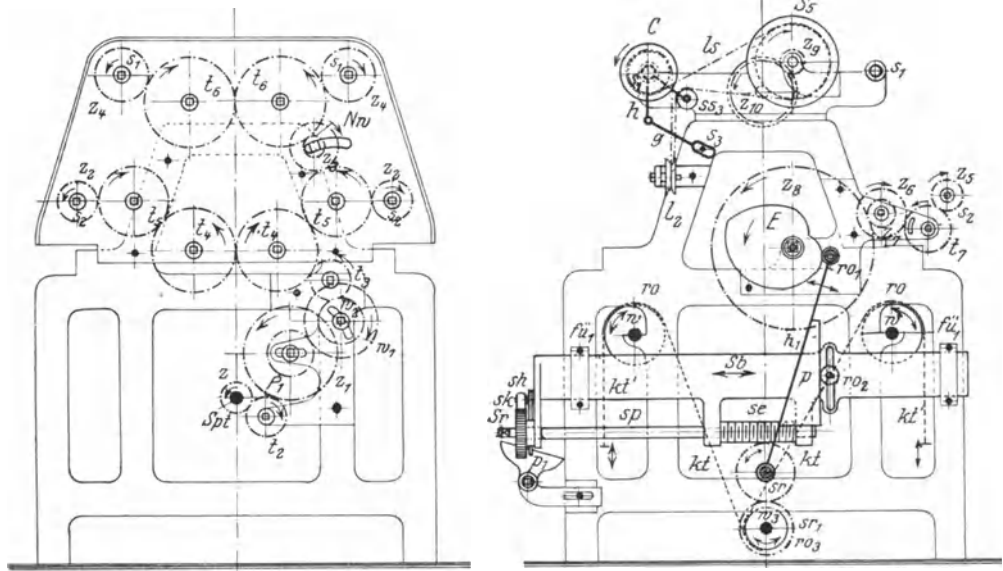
u. 1013. Getriebezeichnungen zur Ringspinnmaschine.
